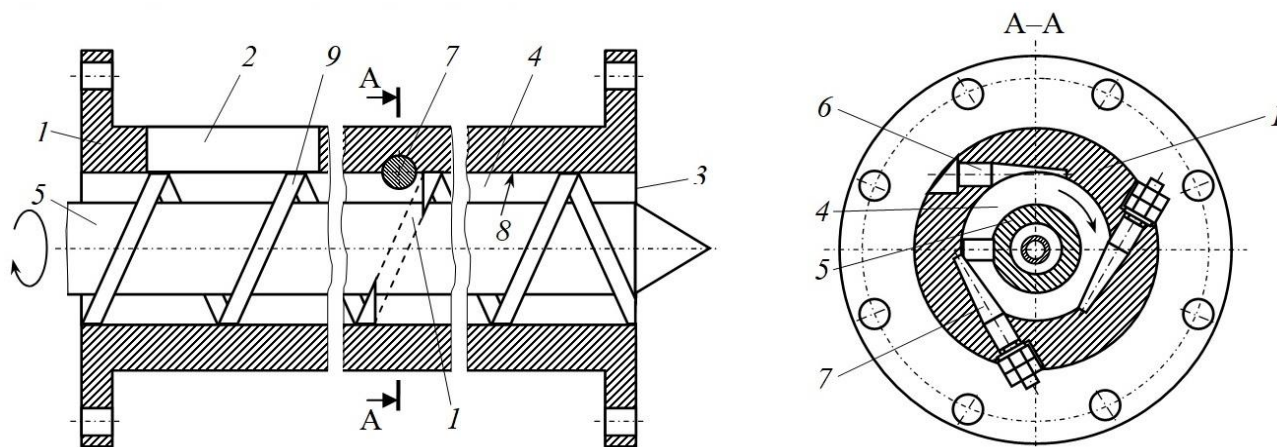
Змішувальна ділянка корпусу одношнекового преса (заявка № u 2026 01851)
